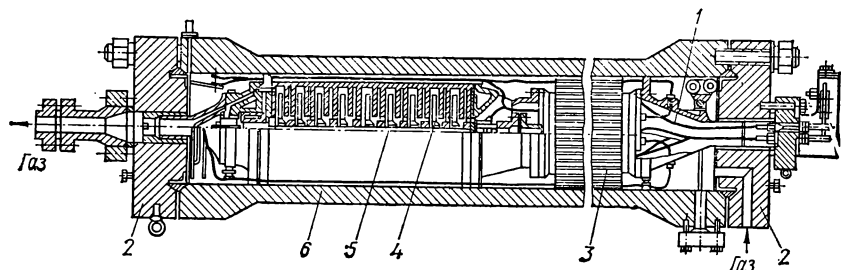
Циркуляционный центробежный компрессор (ЦЦК):
